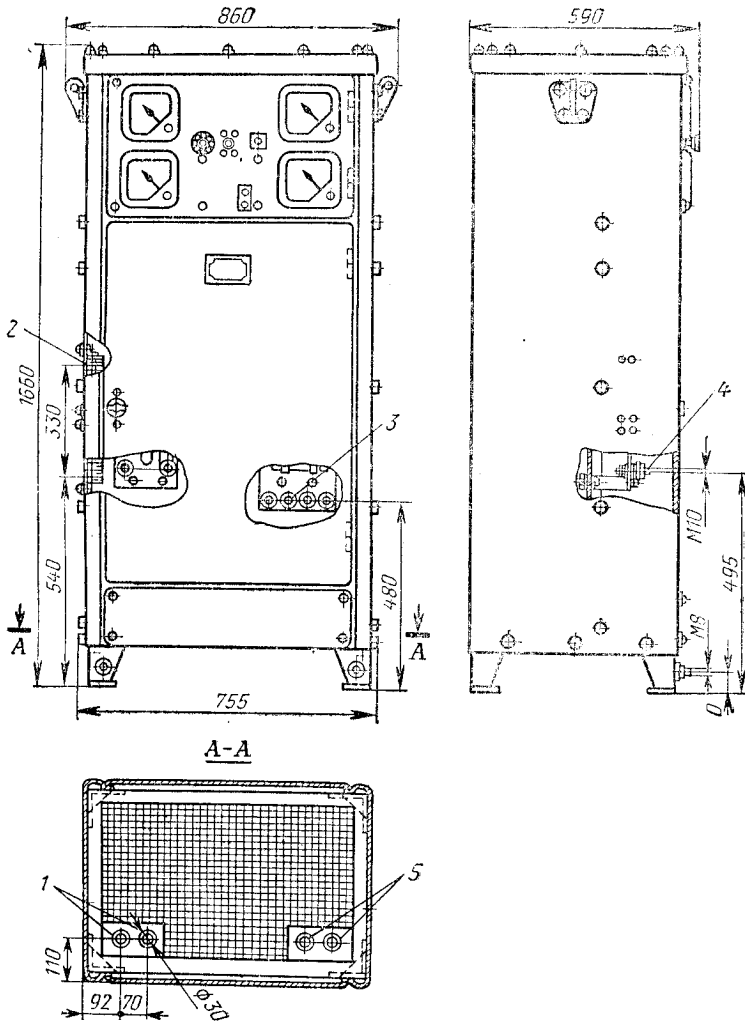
Общий вид и габаритные размеры выпрямительного агрегата ВАЗП-50/245.
